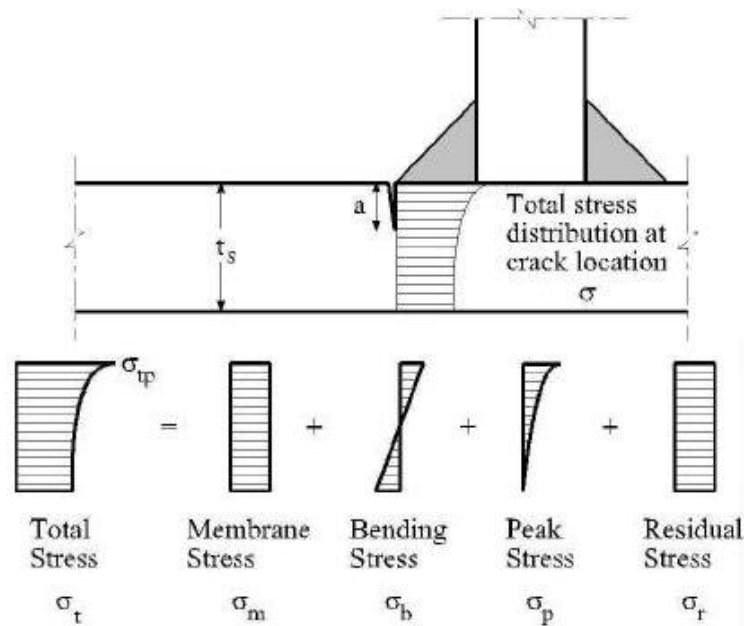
Componentes de tensões em uma junta soldada (SSC, 1999)
